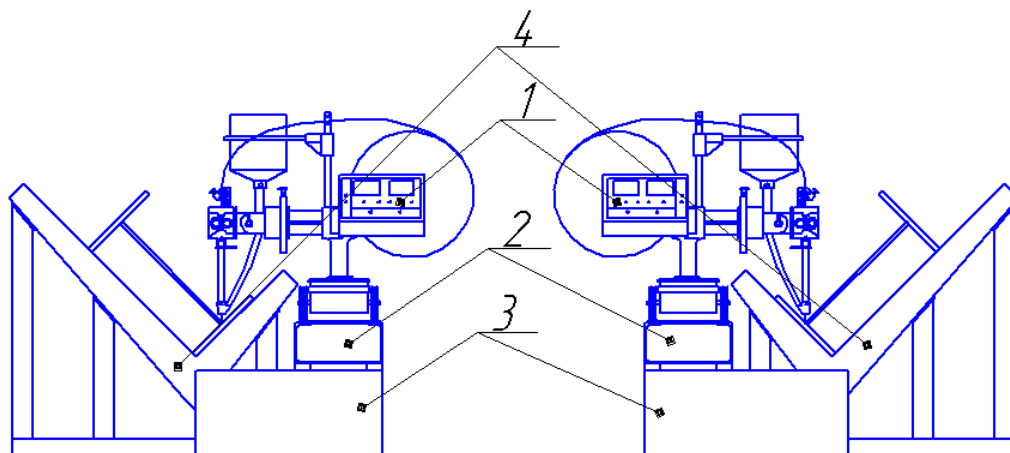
Схема конструкции установки для сварки двутавровой балки
